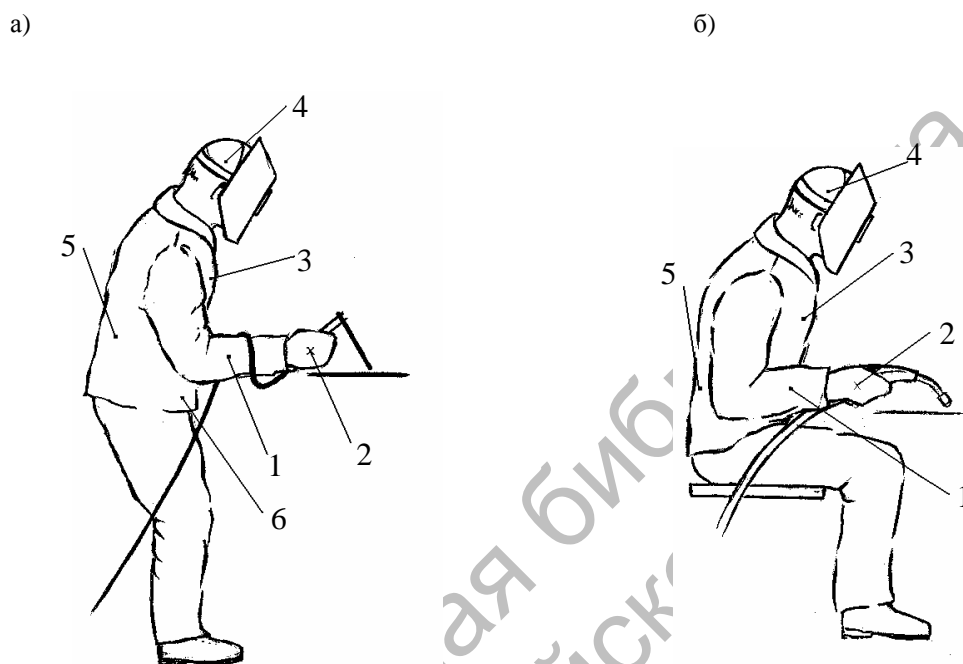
Схема измерений магнитной индукции и действие нагрузок при дуговой сварке: а – ручная дуговая сварка в положении стоя; б – сварка в защитных газах в положении сидя; 1 – установка датчика на предплечье; 2 – расположение датчика на внутренней поверхности кисти; 3 – расположение датчика в зоне сердца; 4 – размещение датчика в области головного мозга; 5 – положение датчика в области почек; 6 – датчик в области репродуктивных органов
